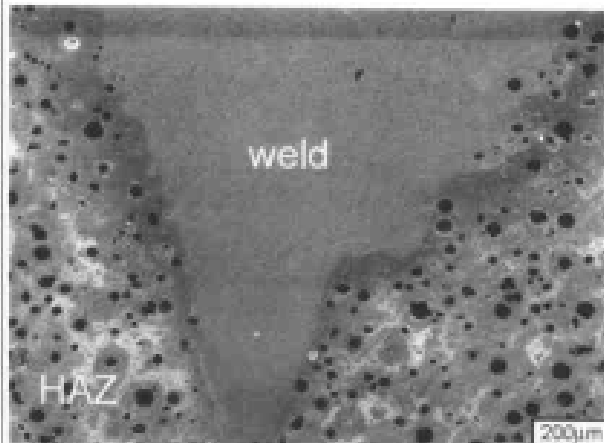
激光焊接, 铸铁, CO<sub>2</sub>激光, 功率3200W, 焦距150mm, 焦点间距0.7mm, 焊接速度1m/min
